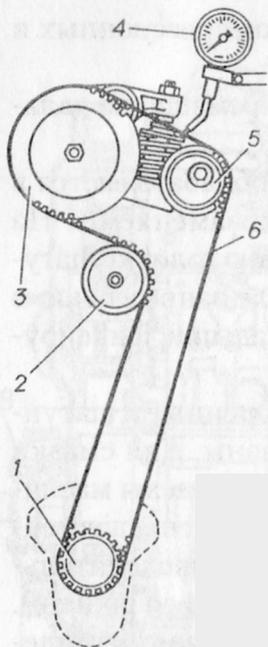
Привод газораспределительного механизма и водяного насоса и установка верхней мёртвой точки:
